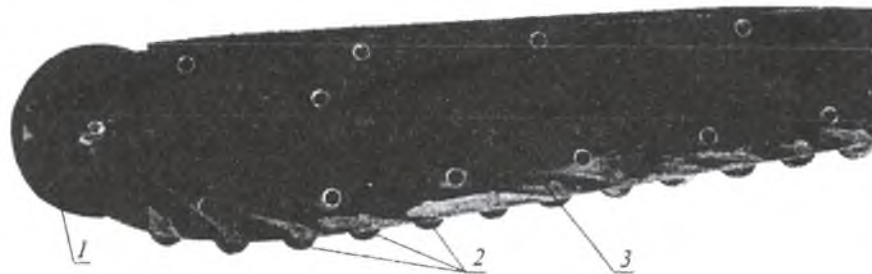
Опытный образец плоской рамы ЦРО клиновидной формы
